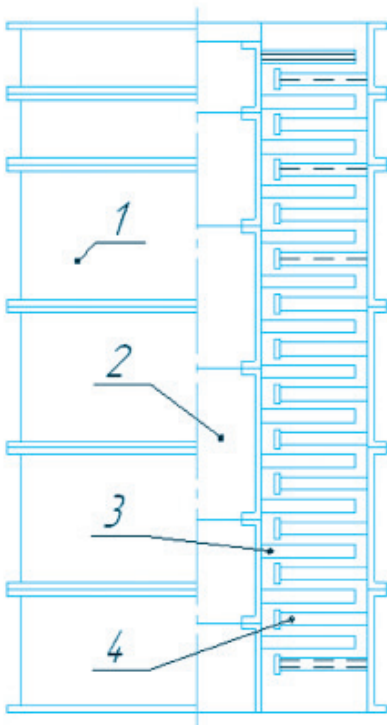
Фрагмент конструкції дифузійного апарата: 1- корпус; 2 – трубовал; 3 – лопать; 4- контролпать.
